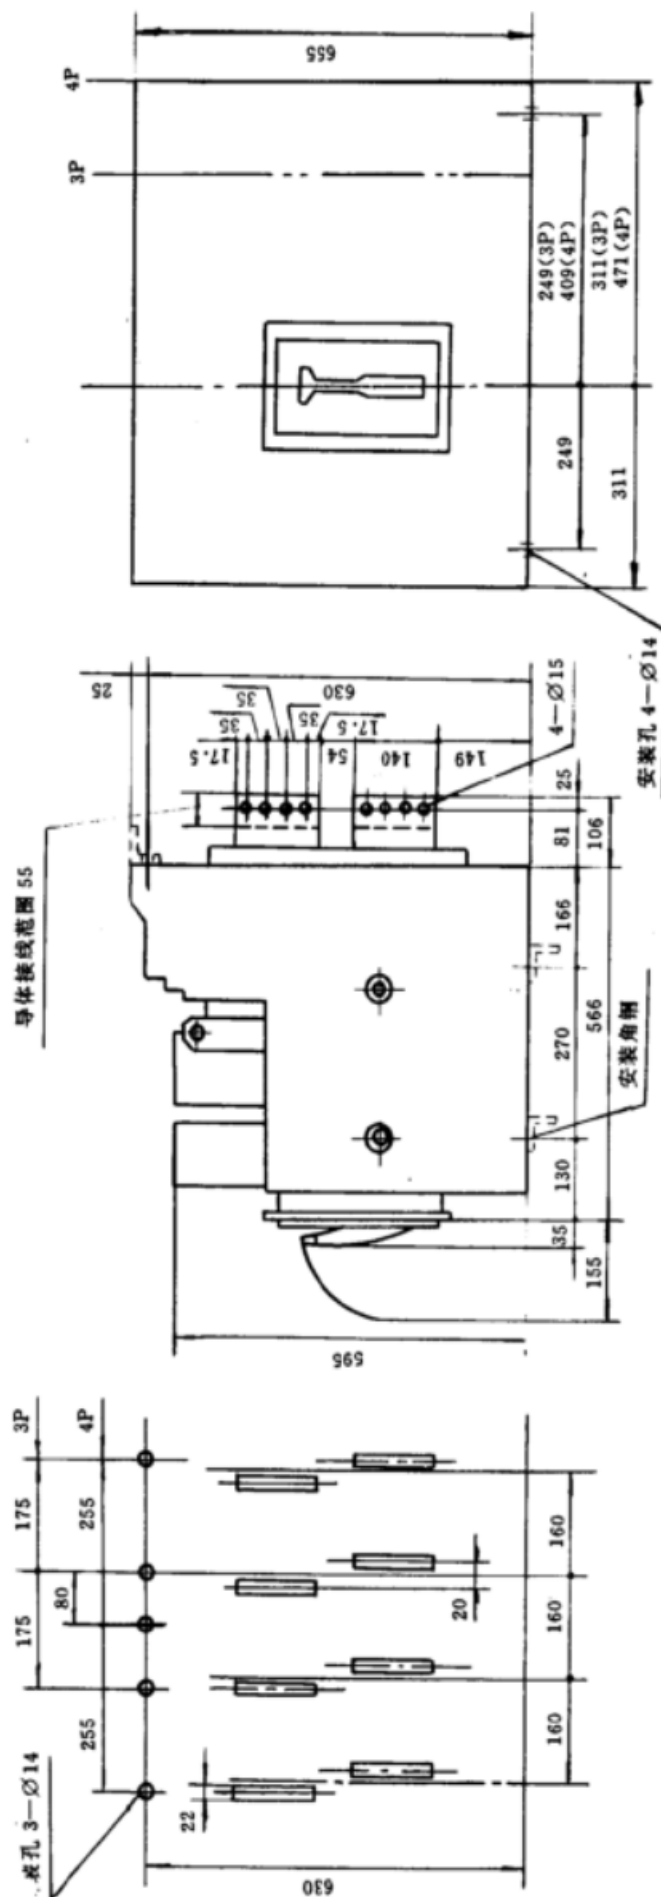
DW 914—4000 船用万能式空气断路器安装及外形尺寸
